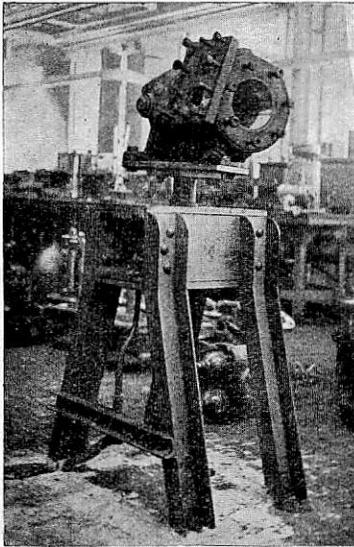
Vorrichtung für die Bearbeitung der Wasserzylinder.
